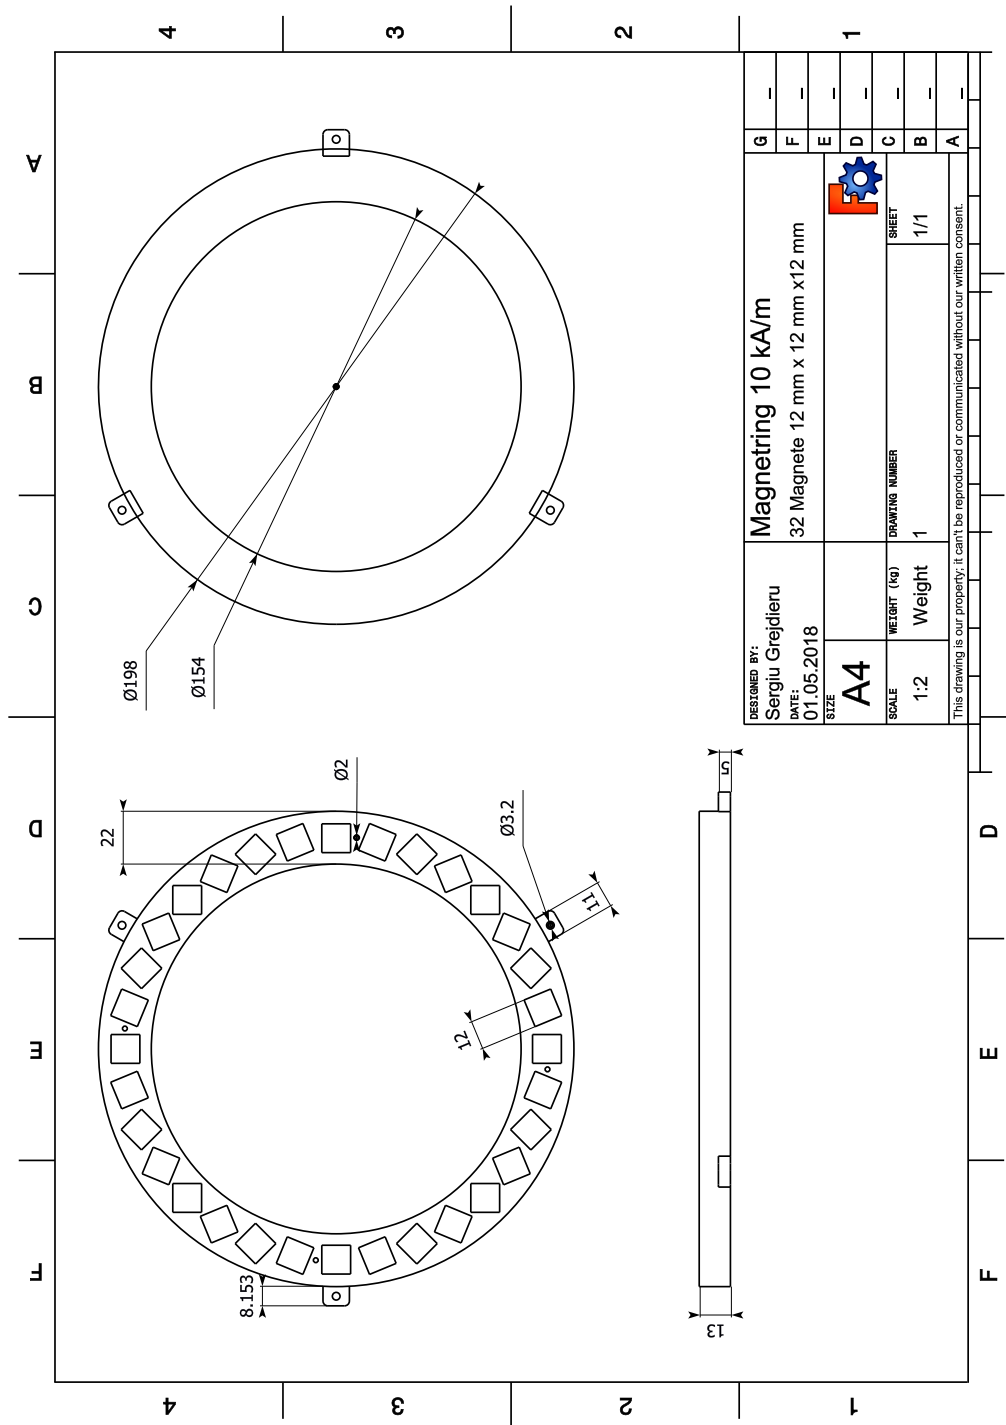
Technische Zeichnung: Magnetring 10 kA/m
